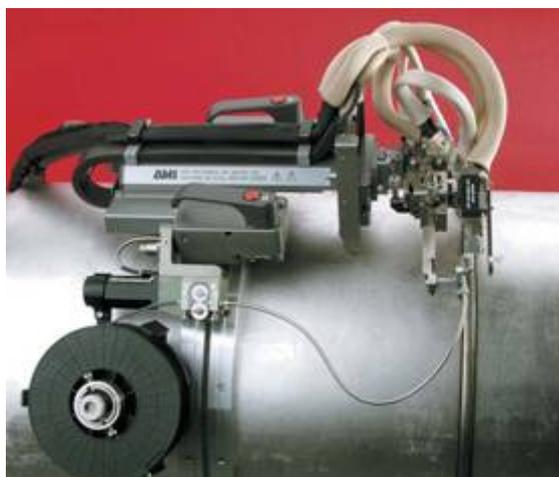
Сварочная головка на направляющем кольце.
